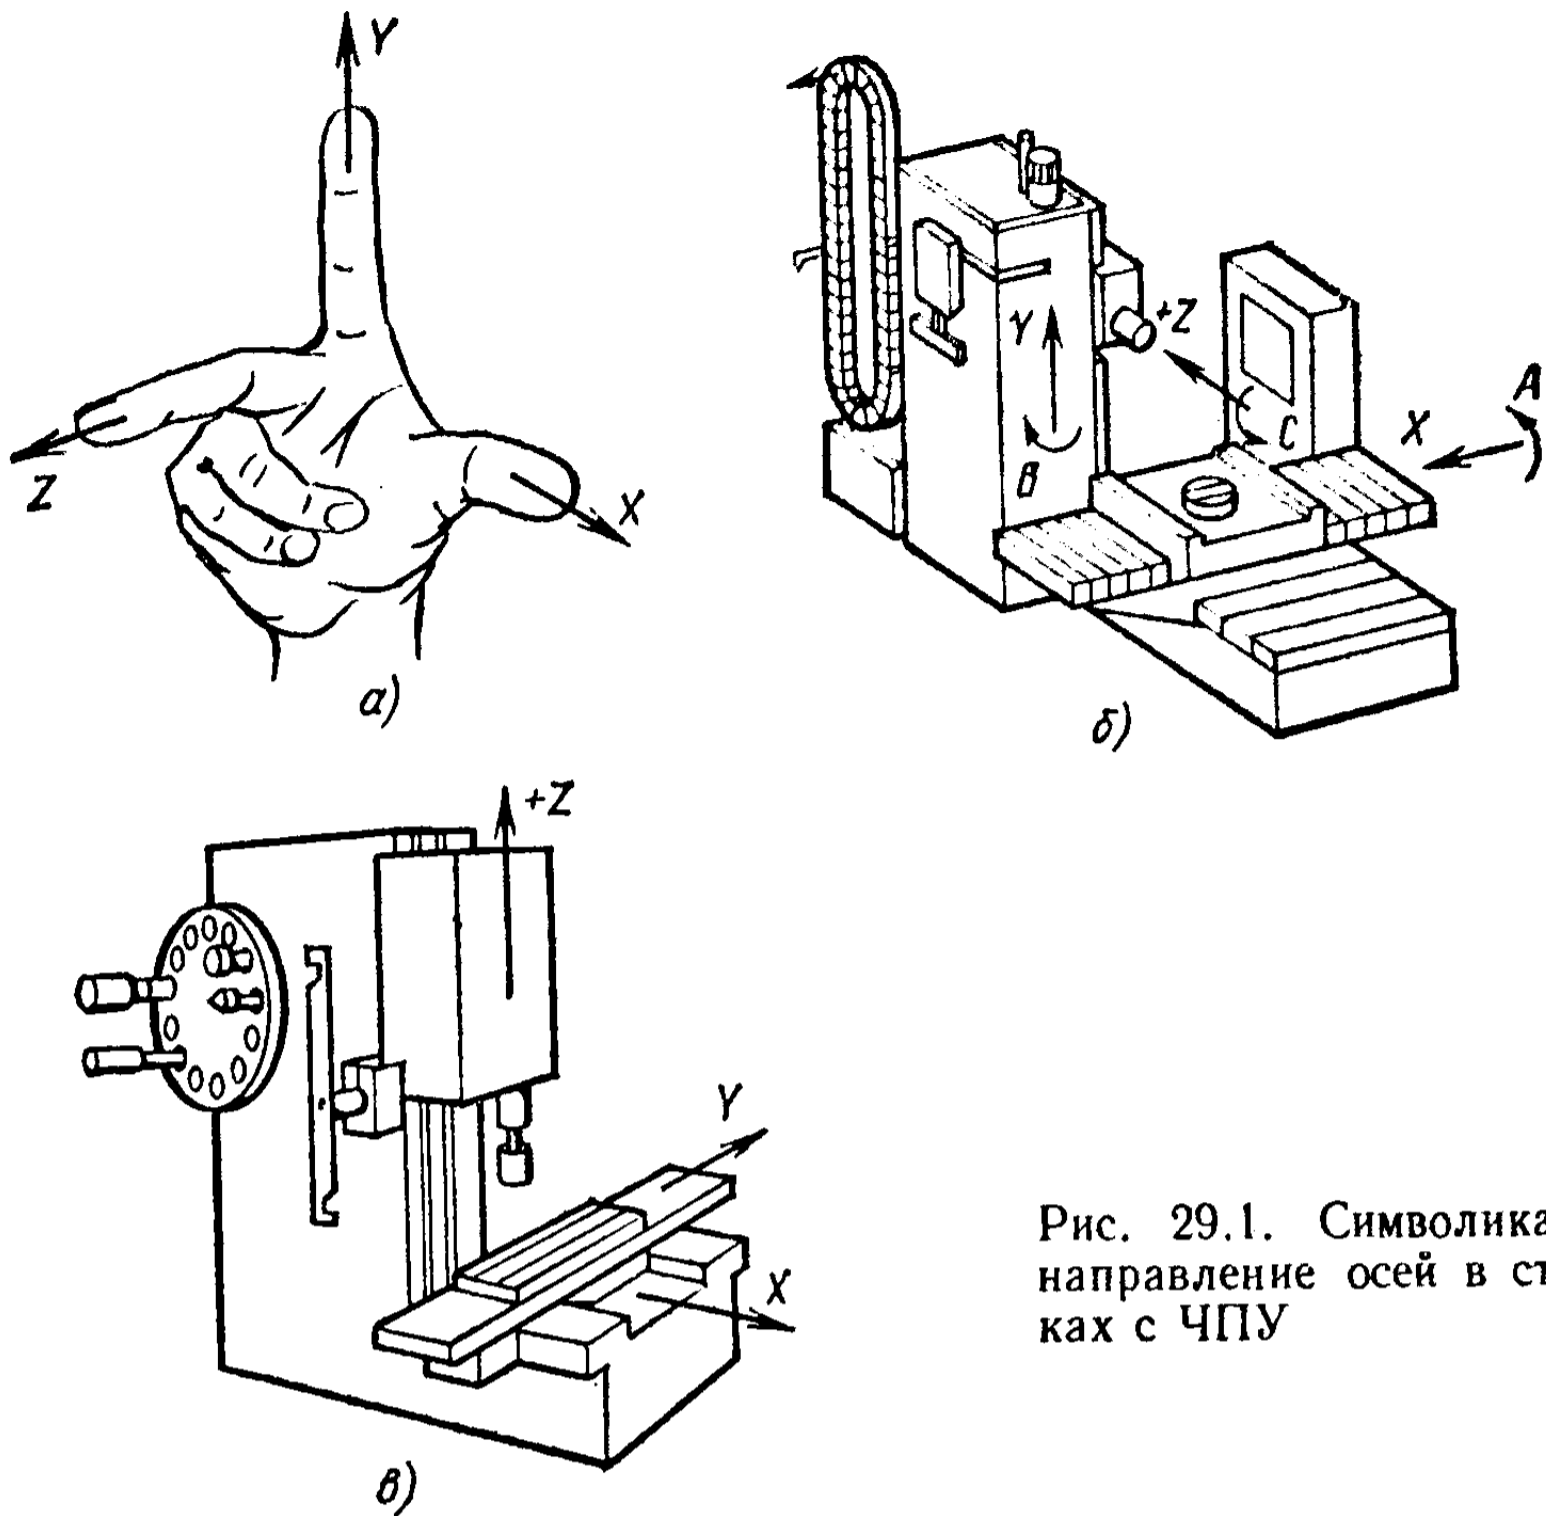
Символика и направление осей в станках с ЧПУ
